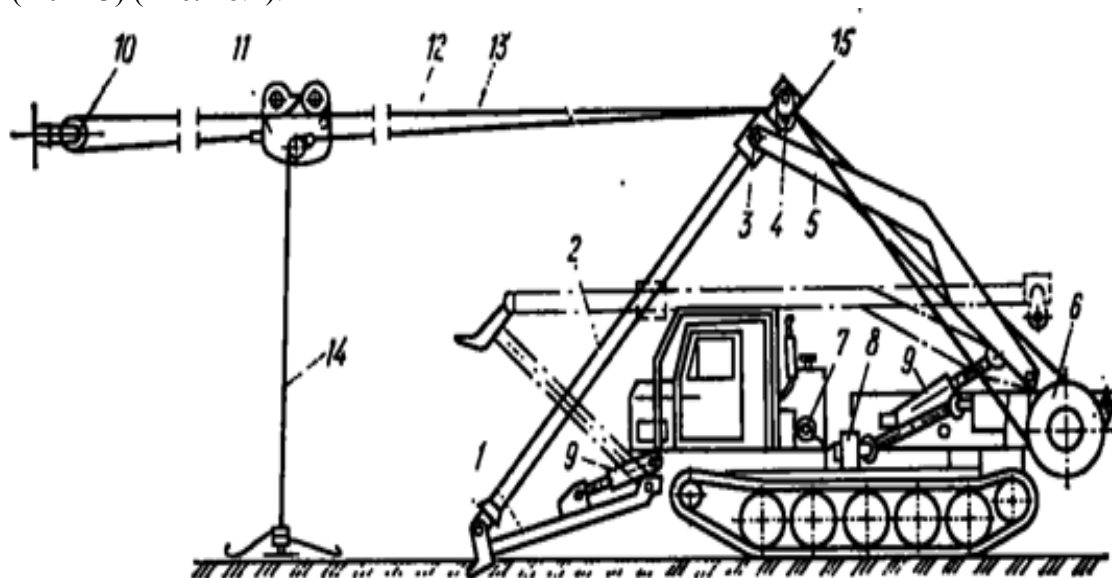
Самоходная канатная установка МЛ-43: 1 — упор; 2 — мачта; 3 — ползун; 4 — головка мачты; 5 — стойка; 6 — барабаны; 7 — лебедка трактора; 8 — привод; 9 - гидроцилиндры; 10 — концевой блок; 11 — тележка; 12 — тяговый канат; 13 — несущее-возвратный канат; 14 - собирающий канат с чекерами; 15 — направляющий блок
